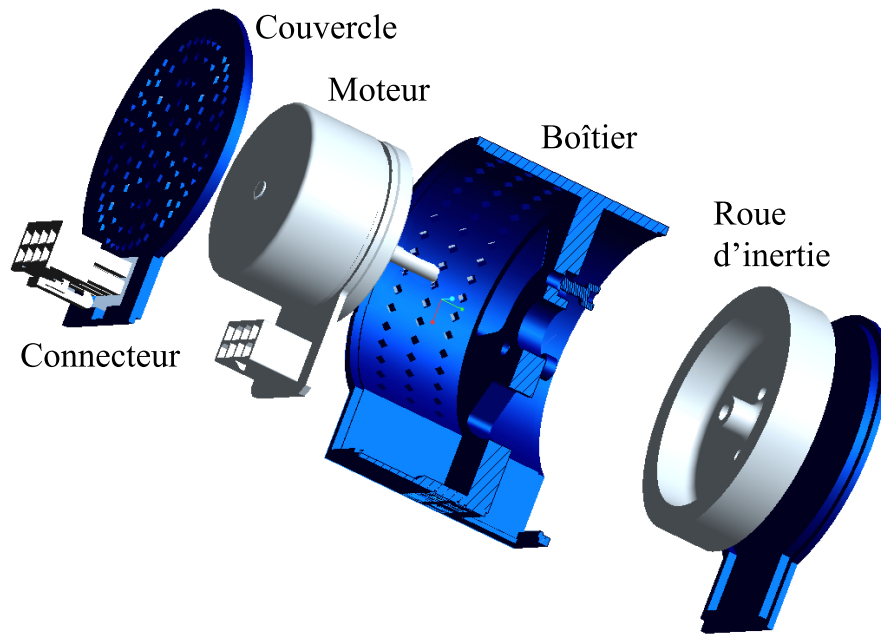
Vue explosée de la boussole haptique en dessin assisté par ordinateur (DAO).
